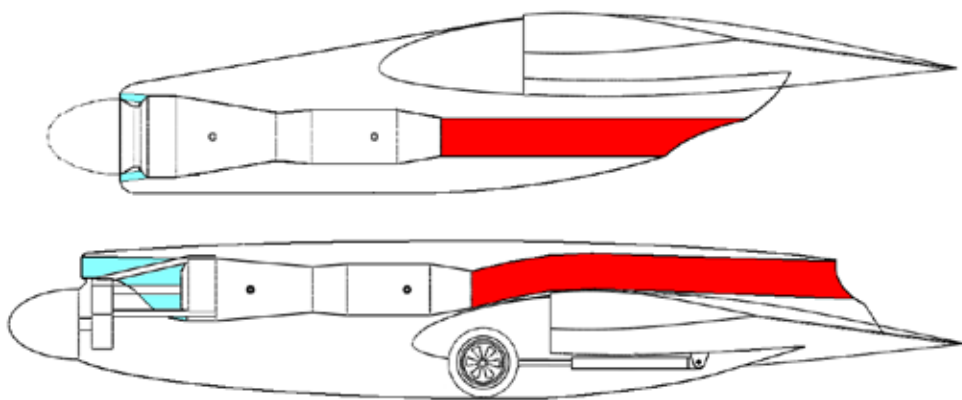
problem instalacji rury wylotowej turbinowego silnika śmigłowego zamontowanego w gondoli przed skrzydłem
